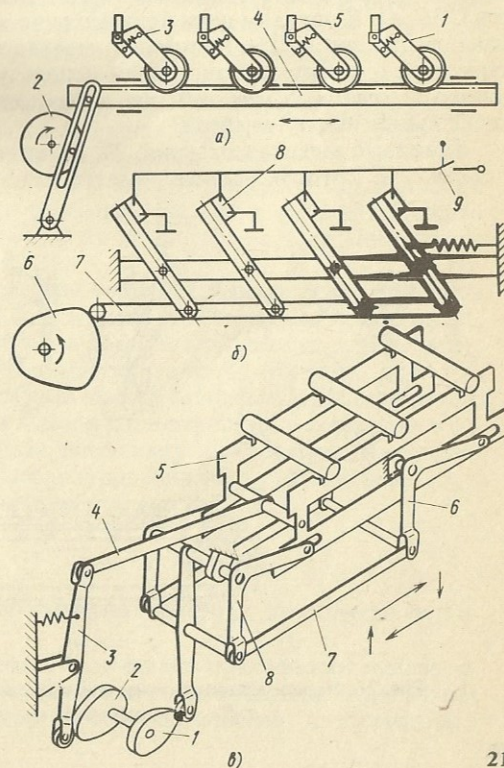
Шаговые конвейеры с реверсивным движением: а — с зубчато-реечной передачей; б — с шарнирным параллелограммом; в — с шагающими линейками
